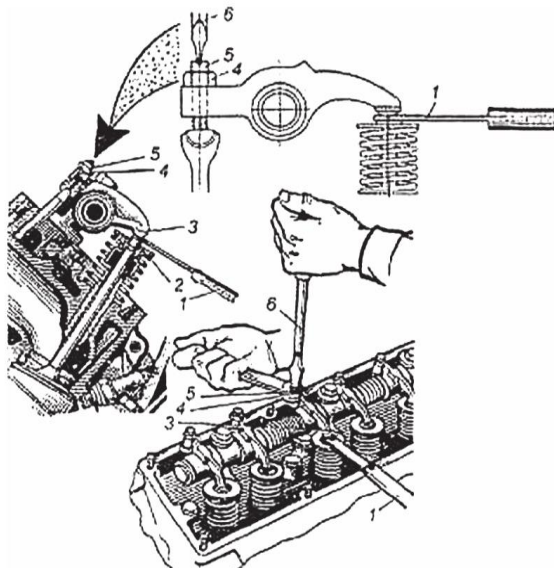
Контроль и регулировка зазоров в клапанных механизмах ГРМ
